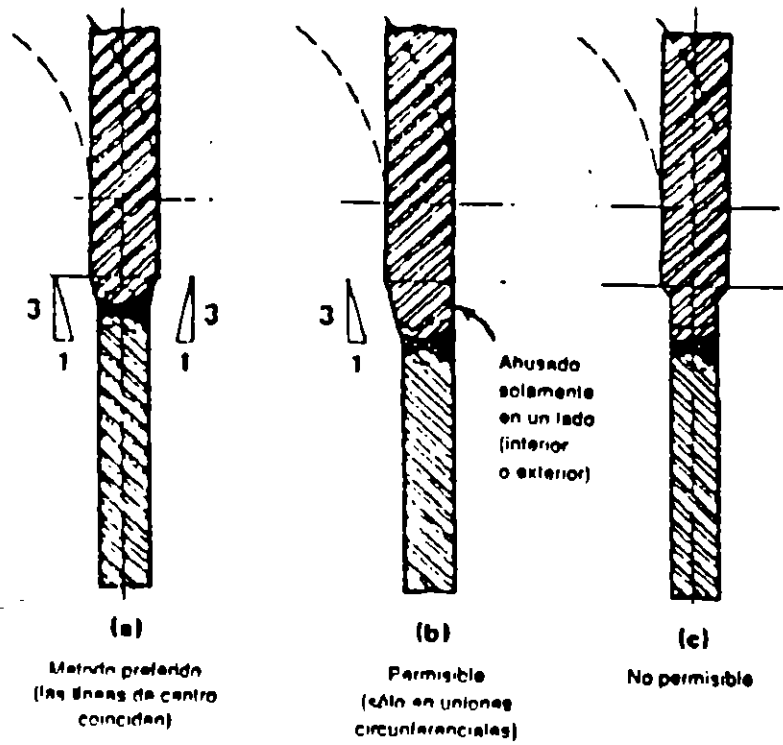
SOLDADURA A TOPE DE PLACAS DE ESPESORES DIFERENTES
